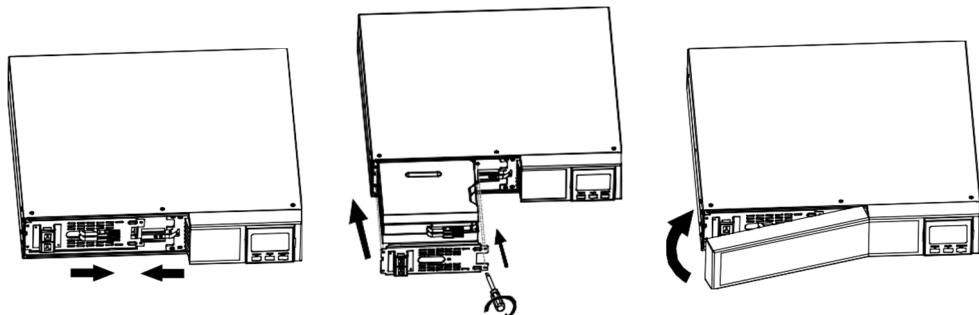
Последовательность установки контейнера с батареей в корпус ИБП
